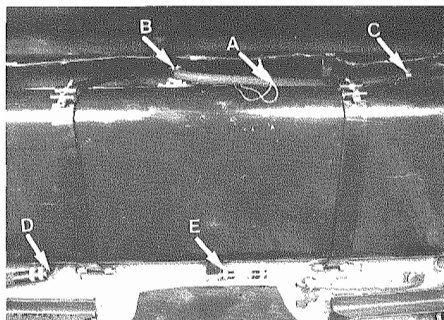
A - Cavi elettrici livello carburante - Electric wires, fuel level
